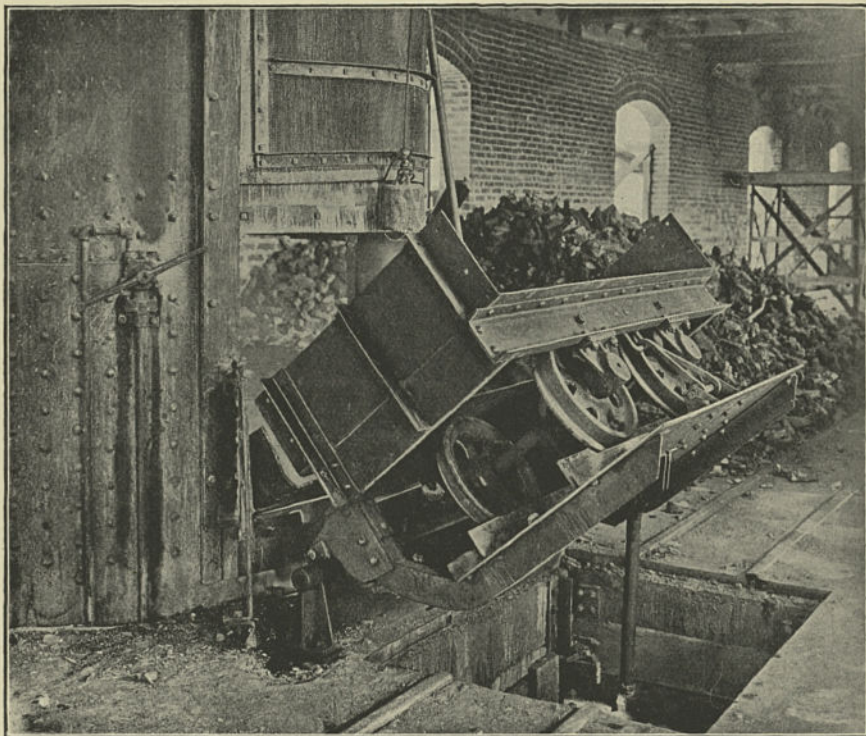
Machine Whiting pour le chargement des cubilots.
